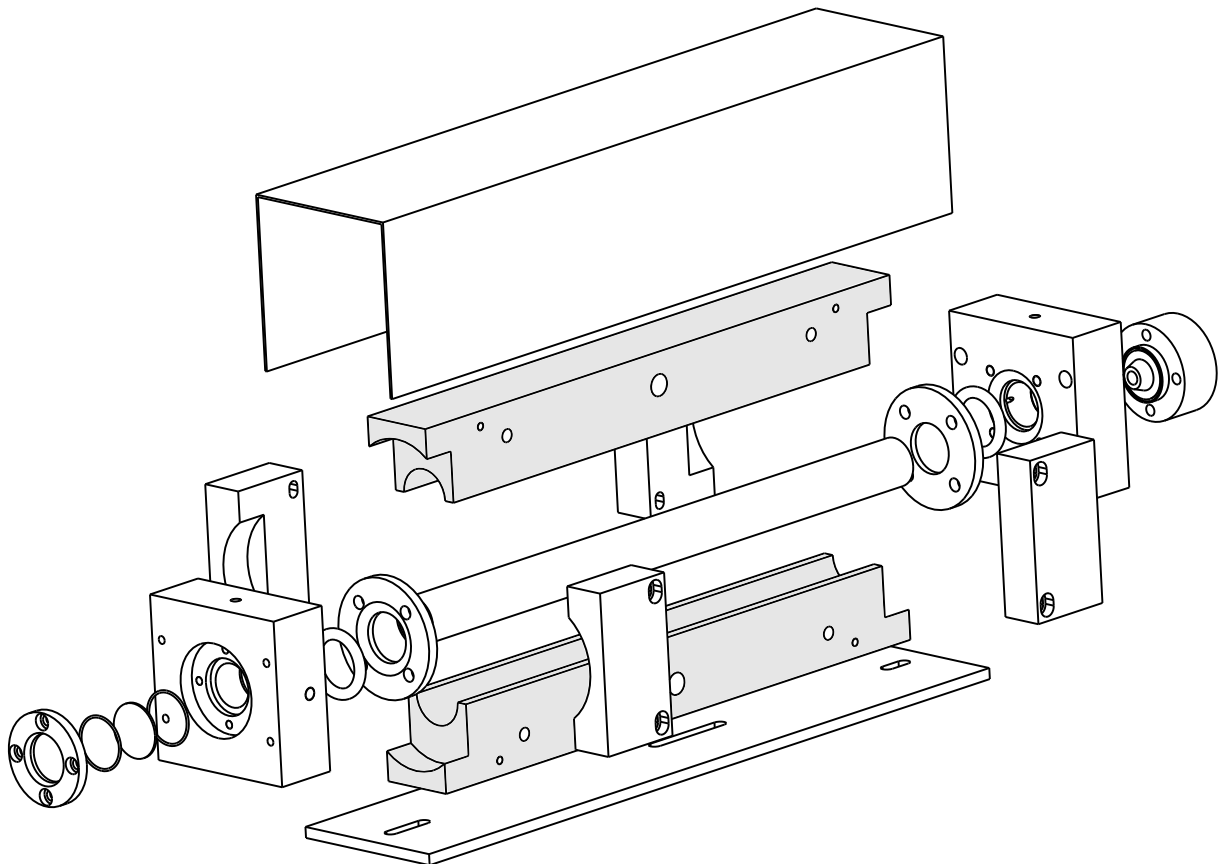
Explosionszeichnung der modifizierten Baugruppe für eine Beheizung der Bestrahlungskammer.
